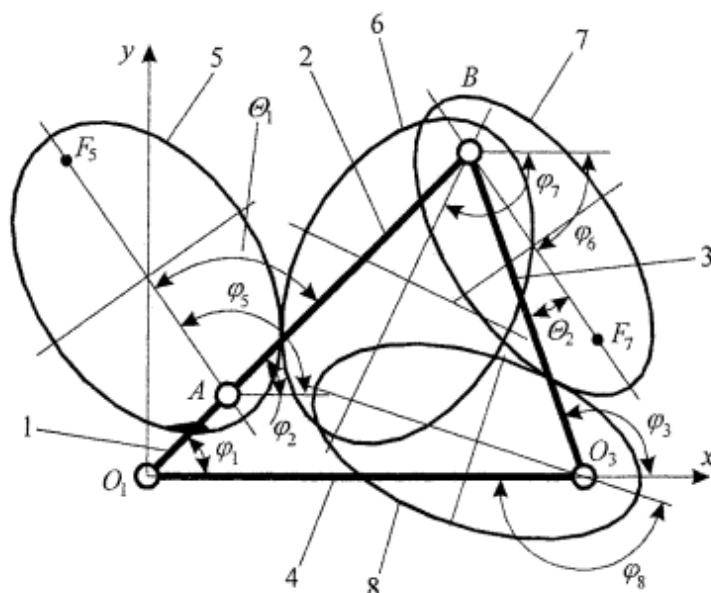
Схема зубчато-рычажного механизма с эллиптическими колесами [9]
